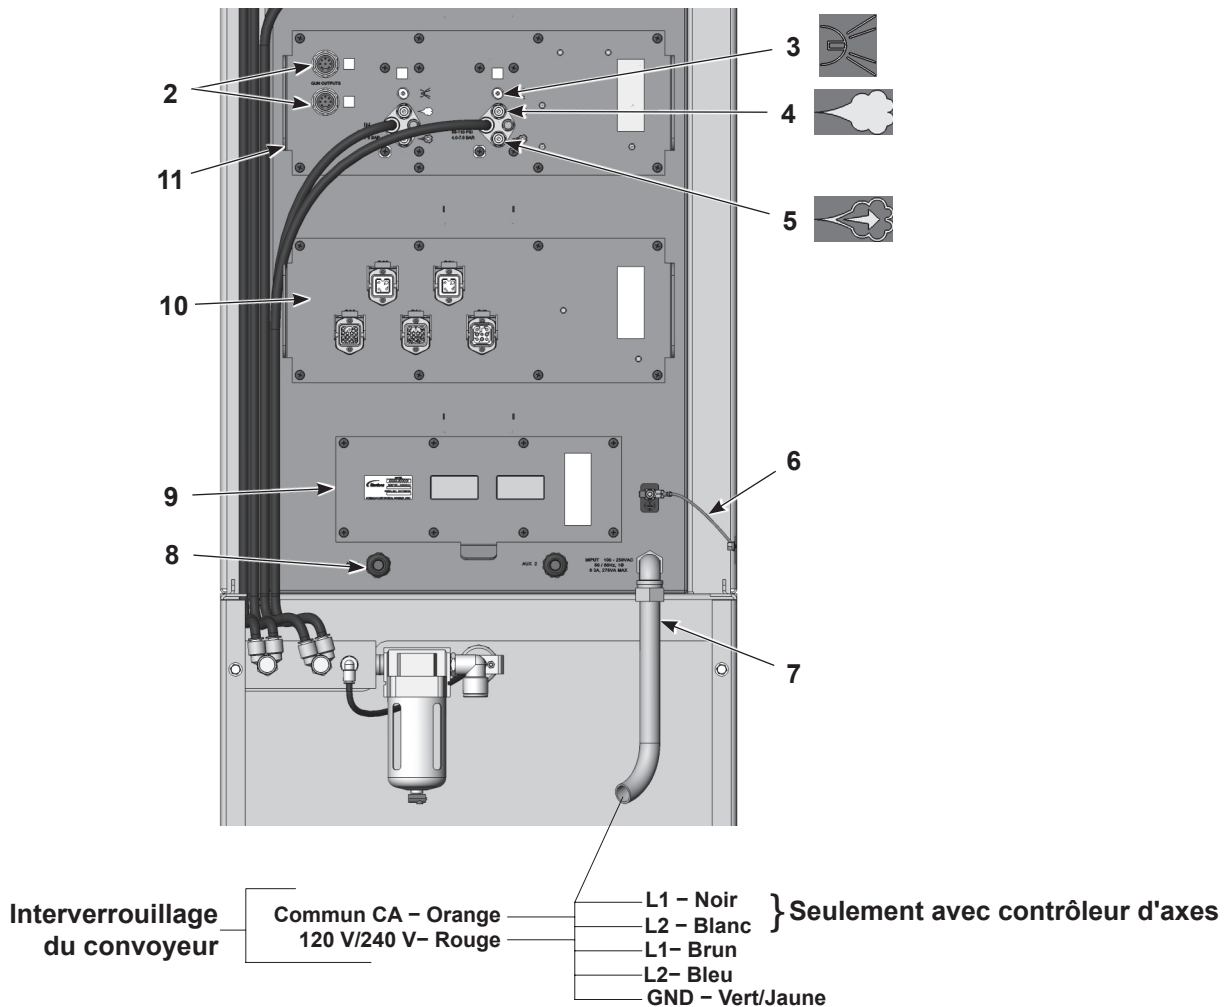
Contrôleur pour plusieurs pistolets – Branchements de l'alimentation, de l'air et du pistolet (capot arrière et panneau actionneur arrière déposés)
